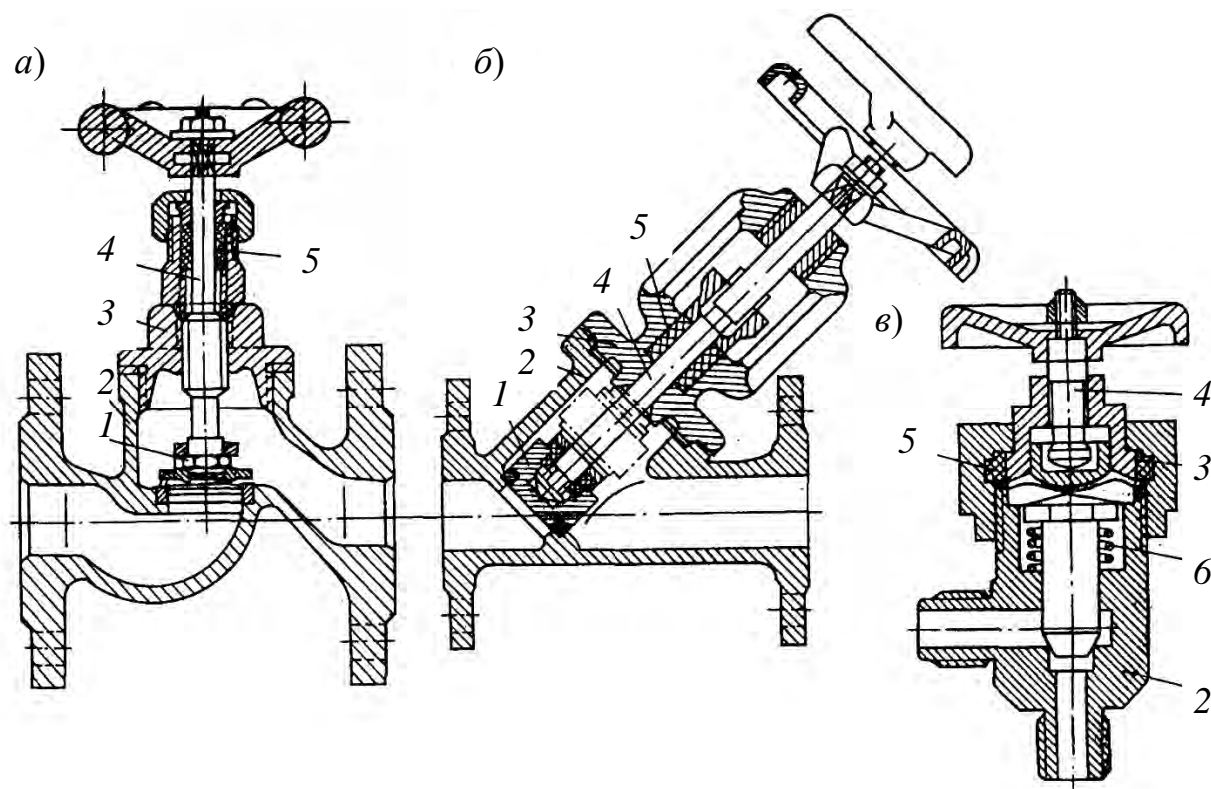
Вентили: *a* – проходной; *б* – прямооточный; *в* – угловой; 1 – тарелка; 2 – корпус; 3 – крышка; 4 – шпindelь (шток); 5 – сальниковая набивка; 6 – пружина
